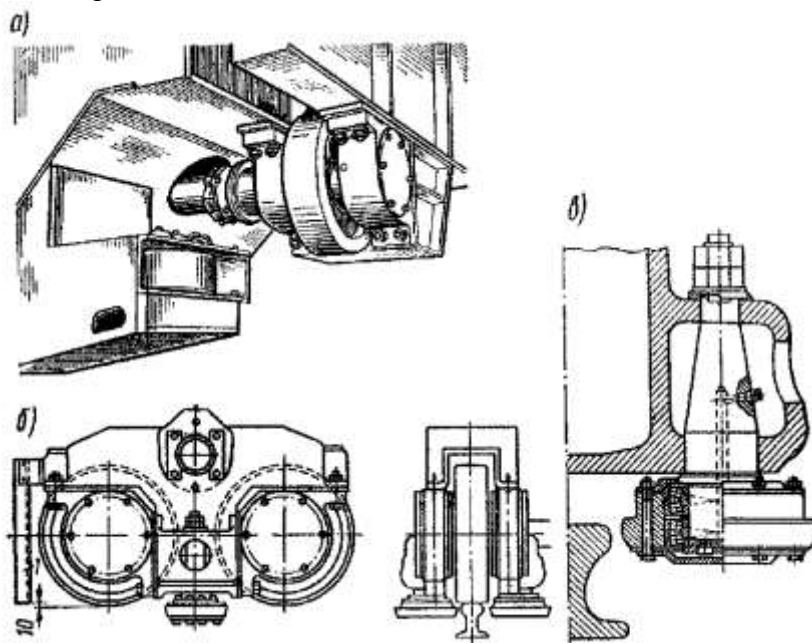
Установка безребордных ходовых колес с направляющими роликами:
